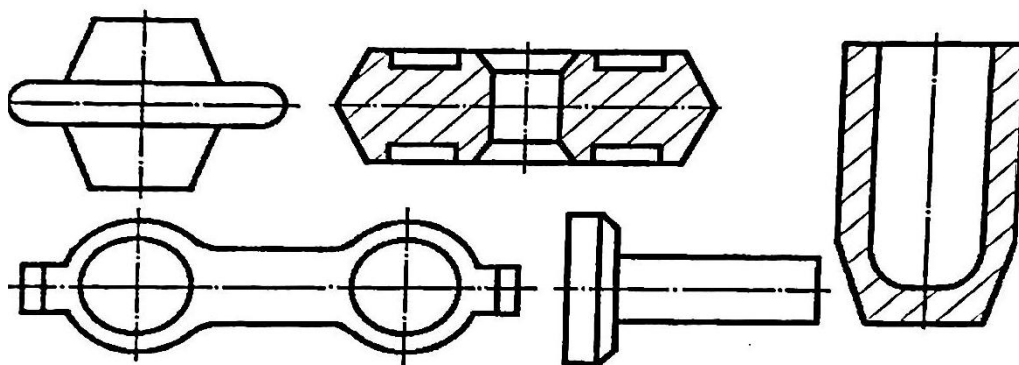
Формы заготовок при штамповке на КГШП.
